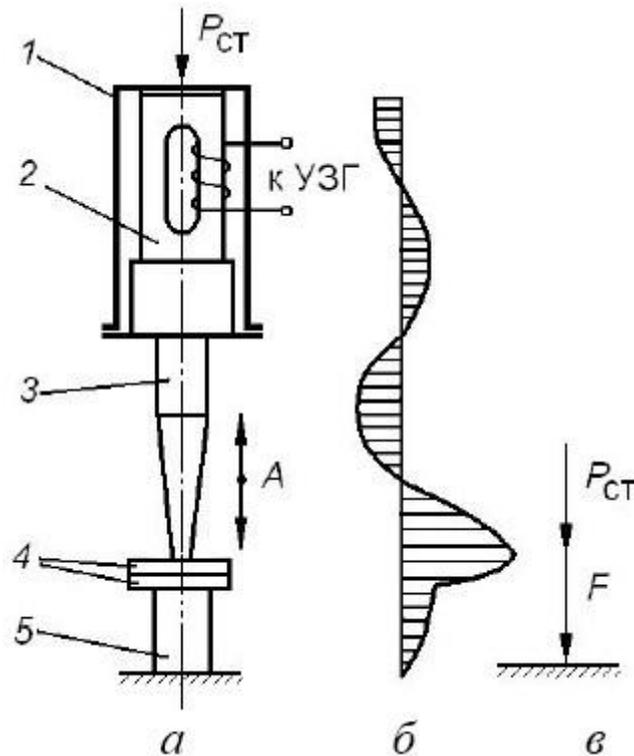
Схема ультразвуковой сварки с нормальным вводом колебаний: а – схема установки; б – эюра амплитуды смещения колебательной системы; в – расположение векторов статического давления $P_{ст}$ и динамического усилия F ; A – амплитуда смещения волновода; 1 – корпус преобразователя; 2 – преобразователь; 3 – трансформатор – волновод; 4 – свариваемые детали; 5 – опора
